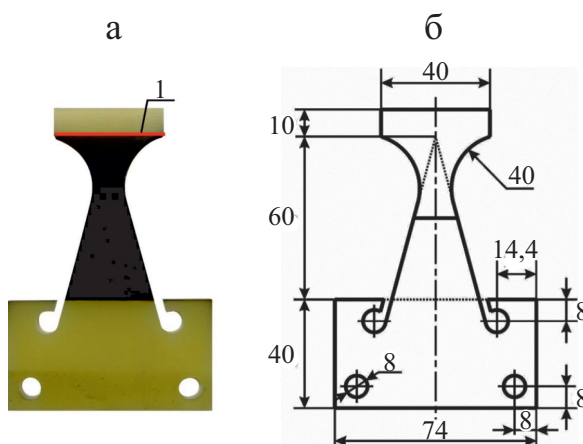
Фотография (а) и рисунок (б) образца для испытаний на знакопеременный изгиб. Линия 1 — линия приложения силы.
